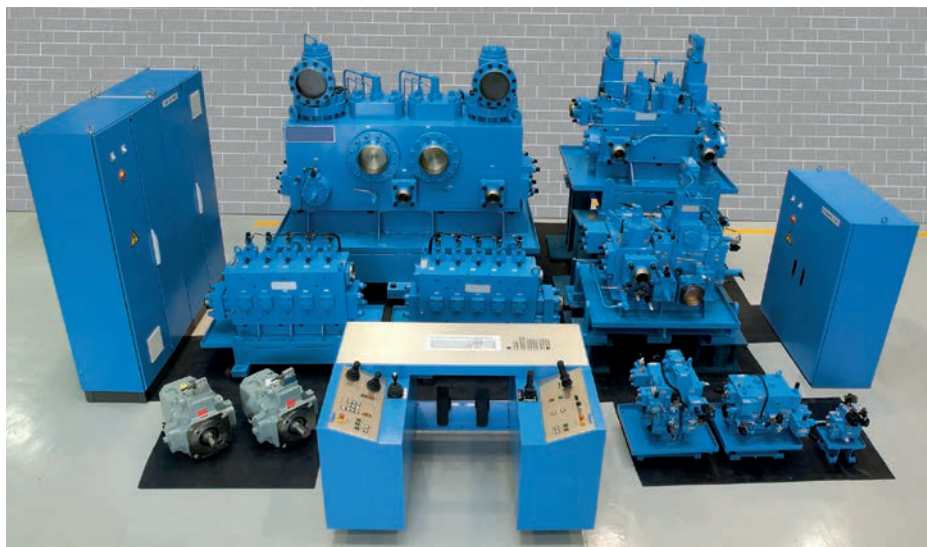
Ausrüstung einer Freiformschmiedepresse auf Mineralölbasis.
